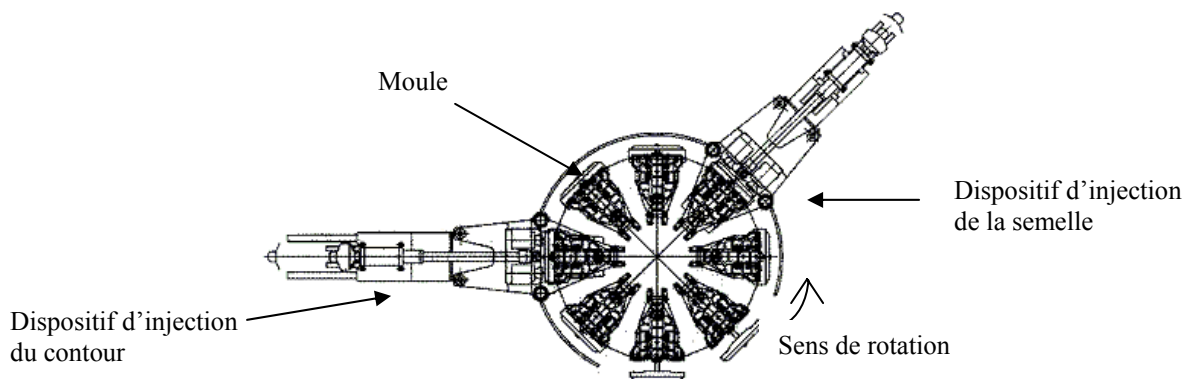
Vue schématique d'une machine à injection à 8 bras.
